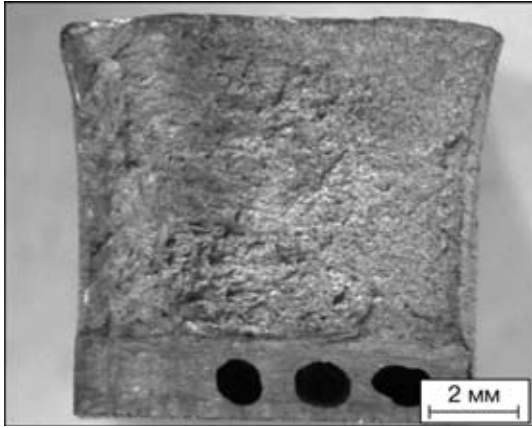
Общий вид поверхности излома пробы, содержащей сварной WIG шов после испытания на ударную вязкость
